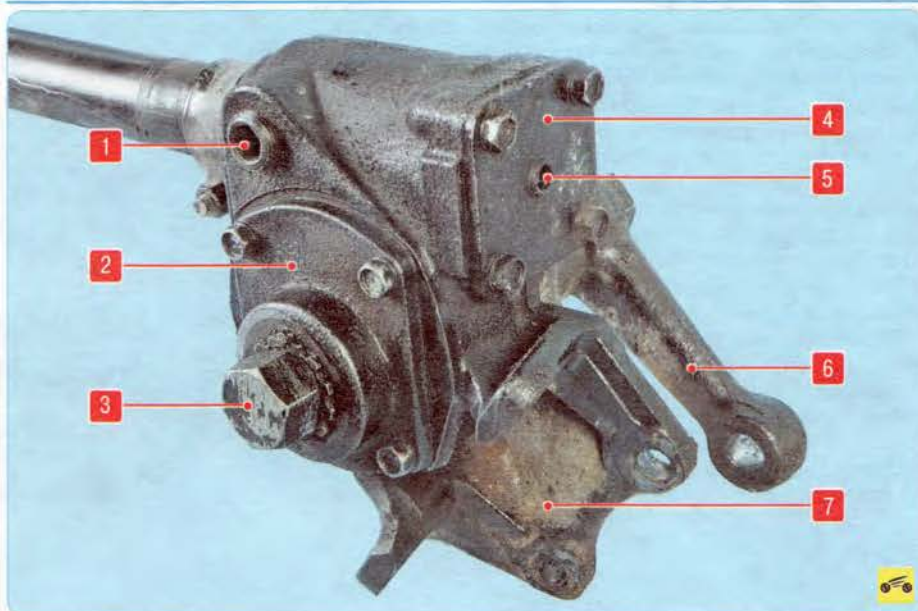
Редуктор рулевого механизма без гидроусилителя (типа червяк-ролик): 1 – пробка наливного отверстия; 2 – боковая крышка редуктора; 3 – гайка вала рычага рулевого механизма; 4 – задняя крышка редуктора; 5 – отверстие провода выключателя звукового сигнала; 6 – рычаг рулевого механизма; 7 – кронштейн крепления
